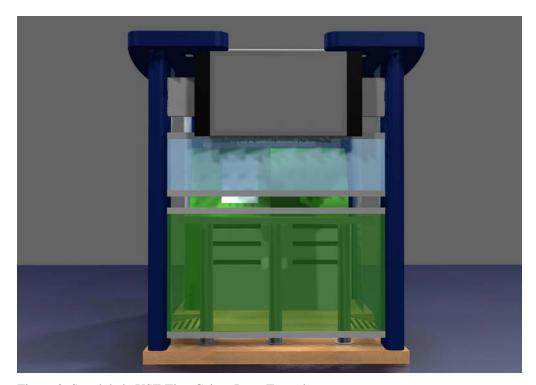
Stand de la USE Tipo Cajero Parte Frontal.
